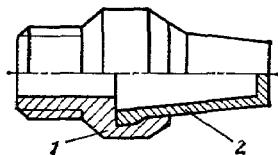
Металлокерамический глушитель типа ГМ1 (1 — штуцер; 2 — металлокерамический стакан)
